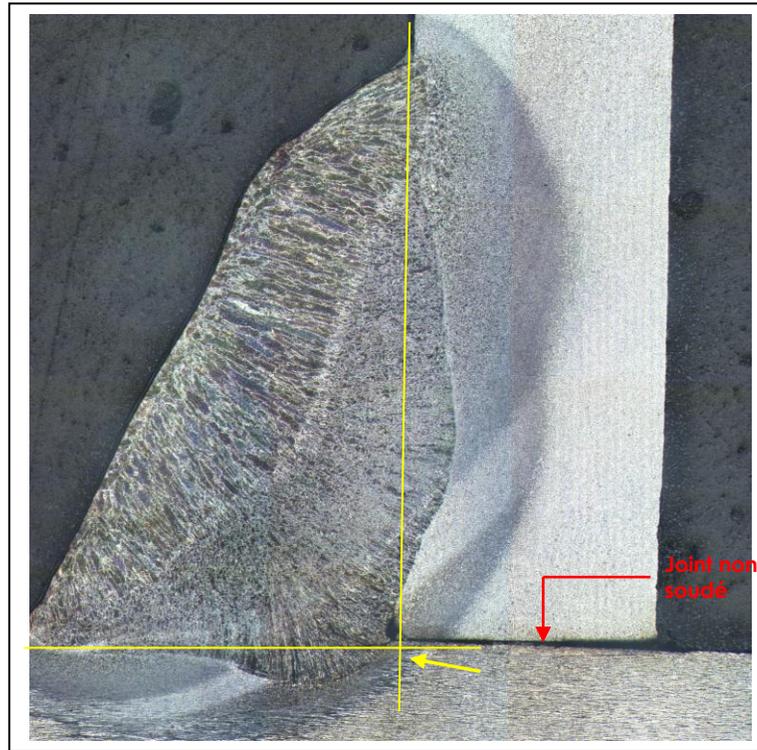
Fissure à la racine du cordon de soudure 2DE - surface int.
